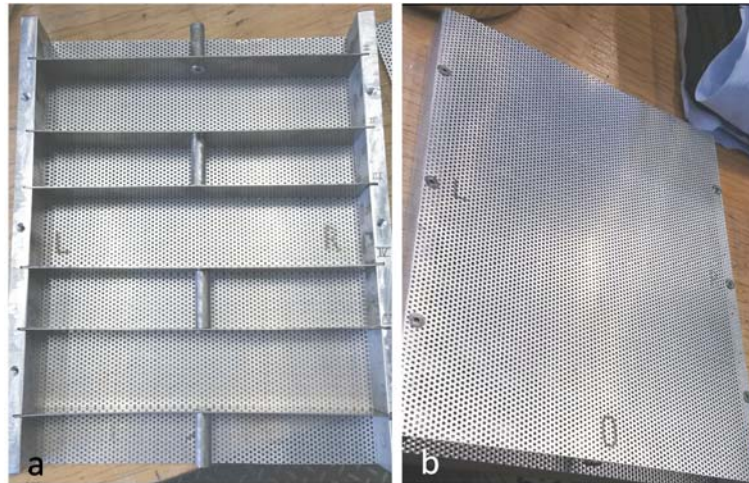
Einlegerwerkzeug (FTA) der zweiten Generation für Balken. a) offen, b) geschlossen.
